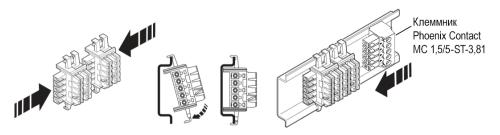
Установка шинных соединителей на DIN- рейку
